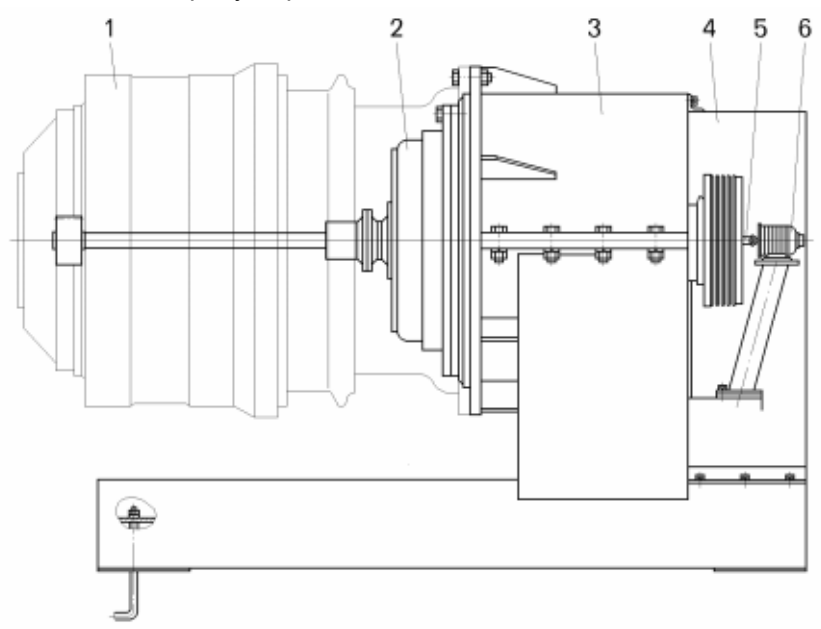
Стенд обкатки редуктора мотор-колеса:
